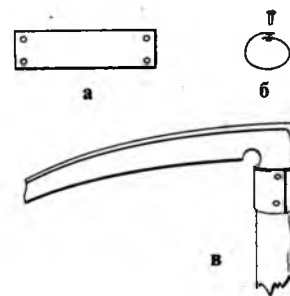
Устройство крепления косы без пятки: а — полоска листовой стали; б — свертывание и клепка; в — крепление лезвия на косовище
